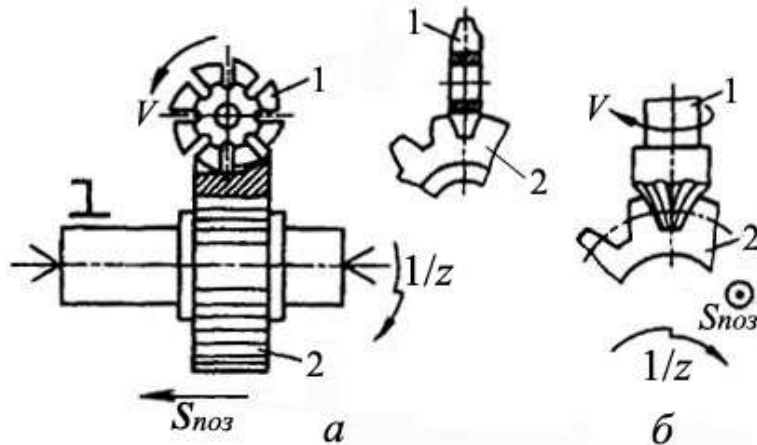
Схеми фрезерування зубців циліндричного колеса методом копіювання
